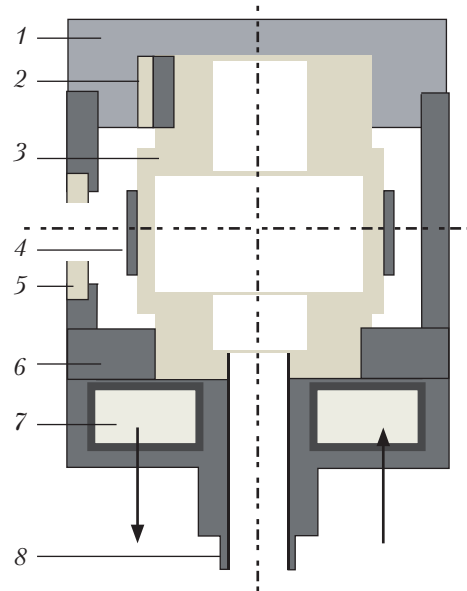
Схема конструкції модуля касети з тримачем фотоприймачів: 1 – кришка касети; 2 – пристрій індикатора номера фотоприймача; 3 – тримач з фотоприймачами; 4 – фотоприймач; 5 – діафрагма; 6 – корпус касети; 7 – пасивний теплообмінник; 8 – привід обертання
